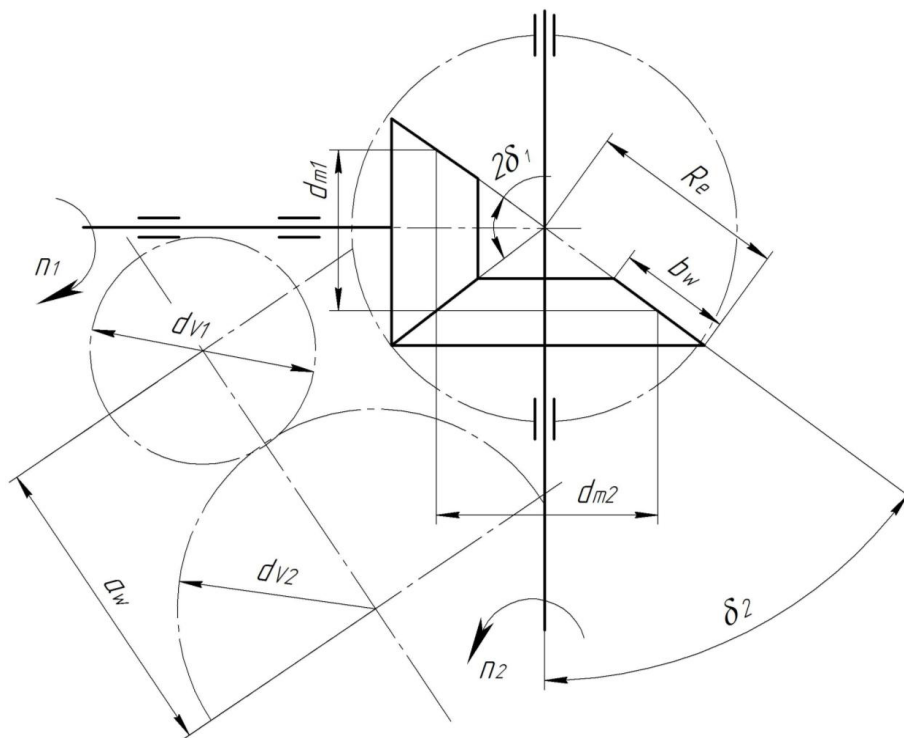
Приведення конічного колеса до циліндричного
